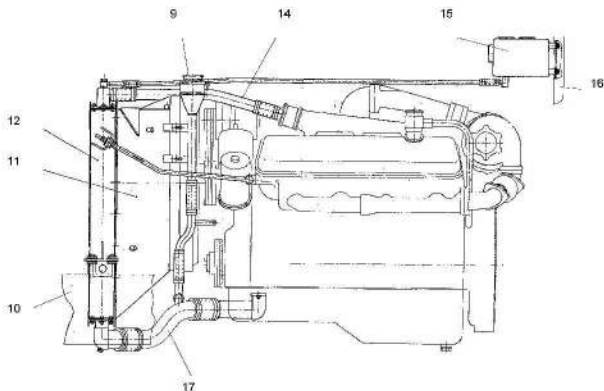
Схема расположения агрегатов системы охлаждения на тракторе: 10 – рама трактора; 11 – кожух вентилятора; 12 – радиатор; 13 – горловина заливная; 14 – выходной патрубок; 15 – бак расширительный; 16 – корпус кабины; 17 – входной патрубок.
